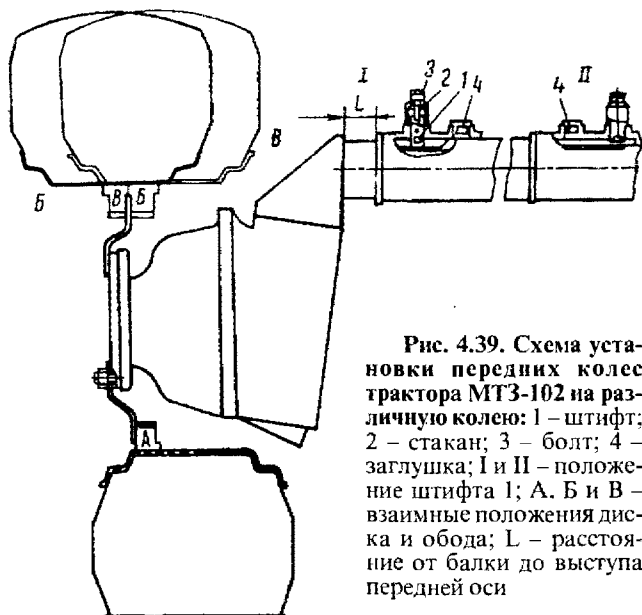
Схема установки передних колес трактора МТЗ-102 на различную колею: 1 — штифт; 2 — стакан; 3 — болт; 4 — заглушка; I и II — положения штифта 1; А, Б и В — взаимные положения диска и обода; L — расстояние от балки до выступа передней оси
